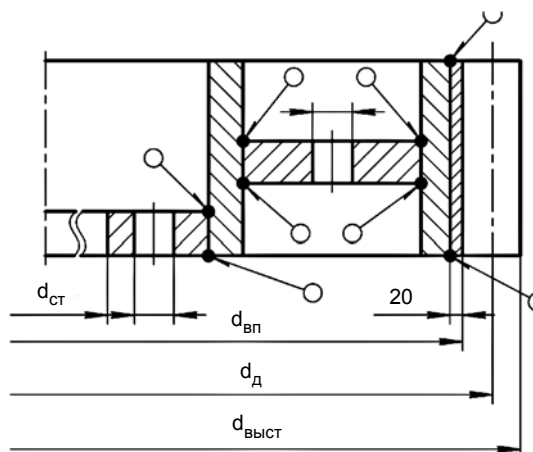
Конструкция корпуса крупногабаритной венцовой шестерни, изготовленной сваркой из стального проката: $d_{ст}$ — диаметр крепежного отверстия ступицы; $d_{вп} = m(z - 2,2)$ — диаметр впадин между зубьями; $d_{н} = m(z + 2)$ — наружный диаметр зубьев (диаметр выступов); $d_{д} = mz$ — диаметр делительной окружности венца; $h_1 = m$ — высота ножки зуба; $h_2 = 1,1m$ — высота головки зуба
